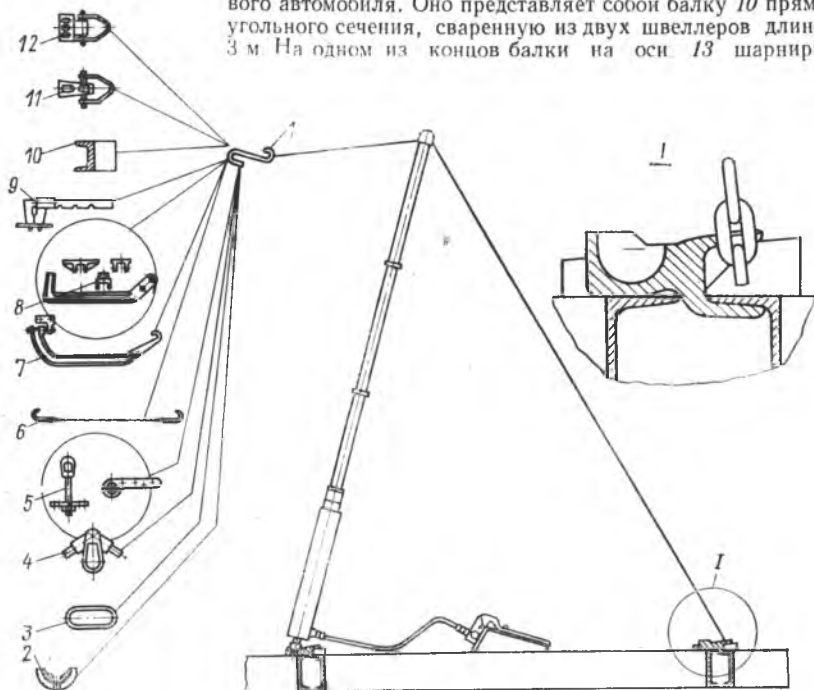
Варианты крепления приспособлений к силовой стойке стэнда Р-620:
